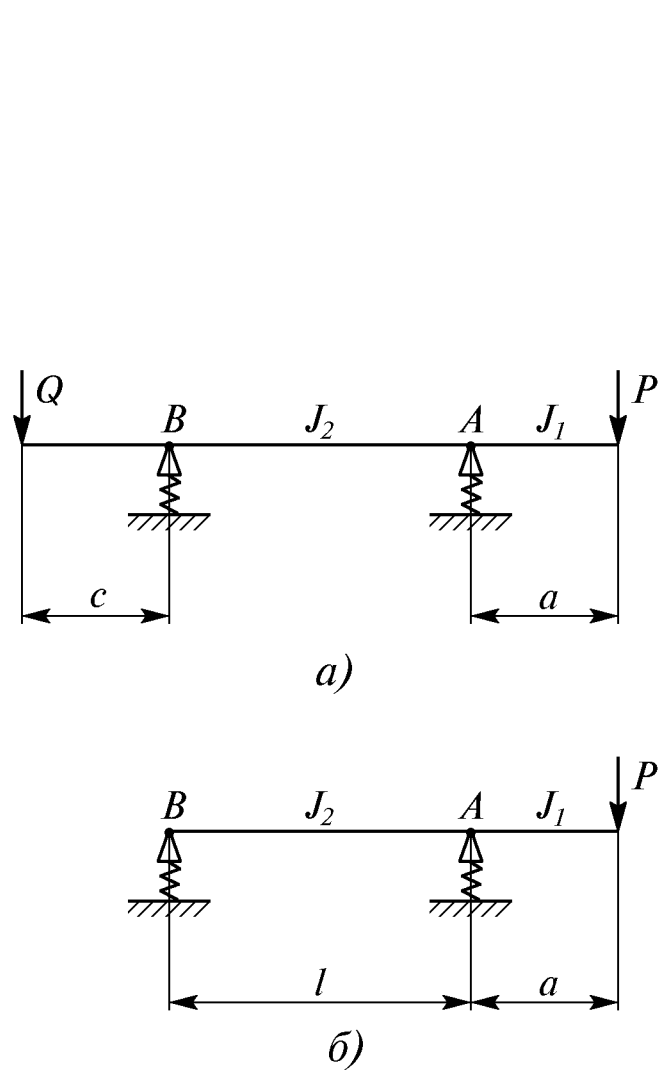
Схемы к расчету шпиндельного узла на жесткость
